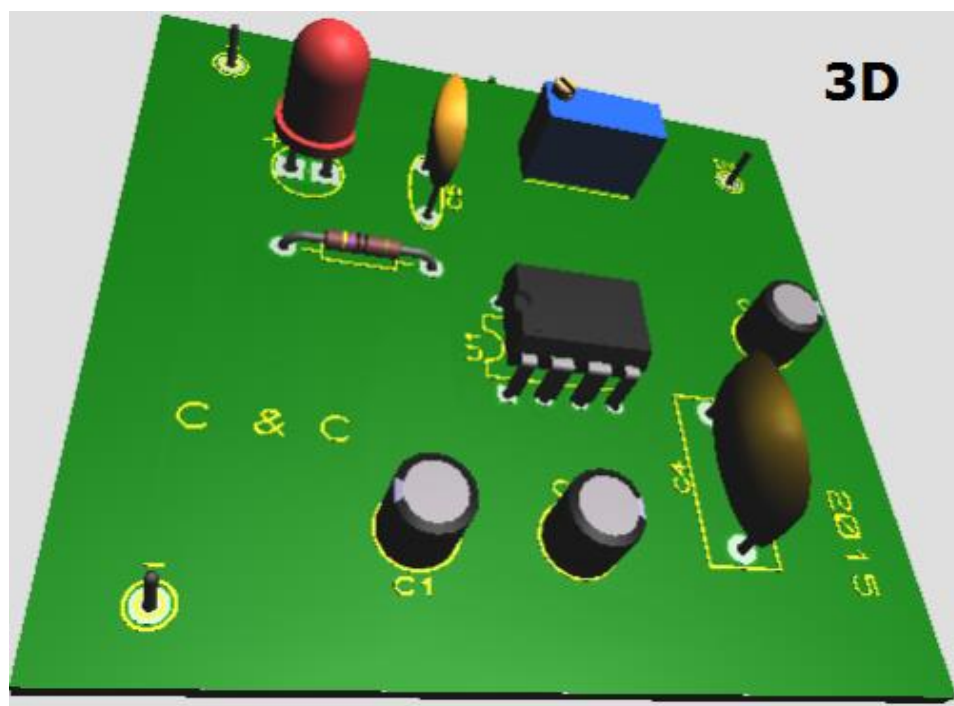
Vista 3D de PCB diseñada para el receptor
